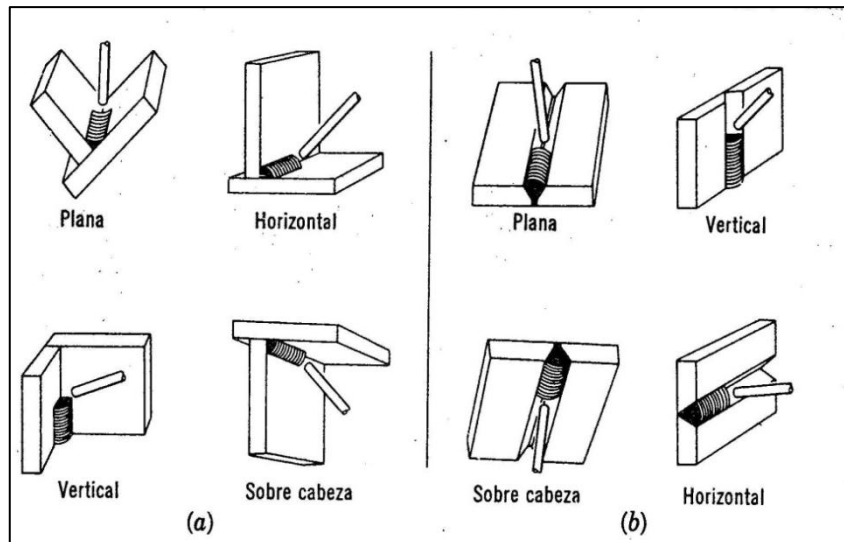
Posiciones al soldar (a) De filete (b) A tope
